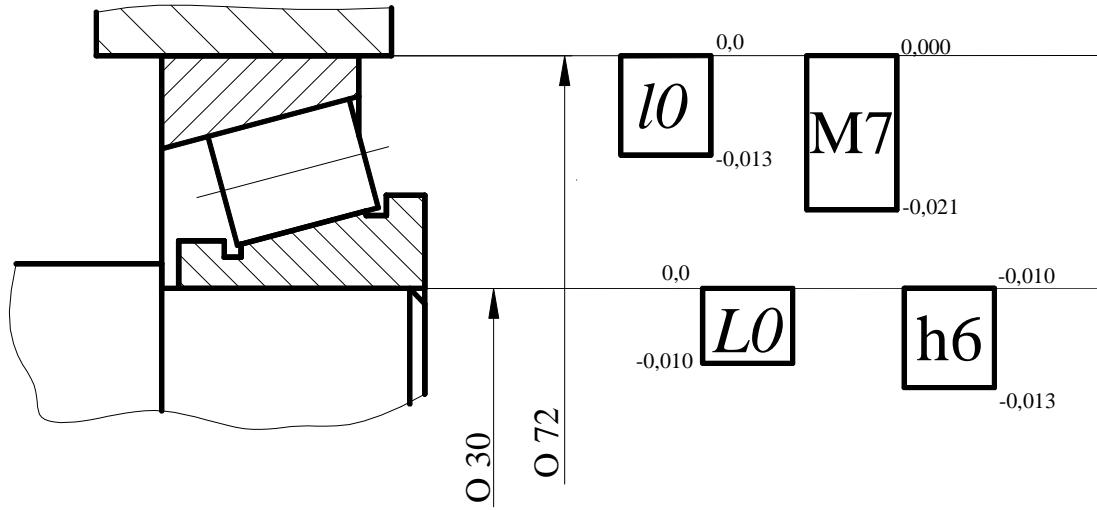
Эскиз подшипникового узла и схема расположения полей допусков
